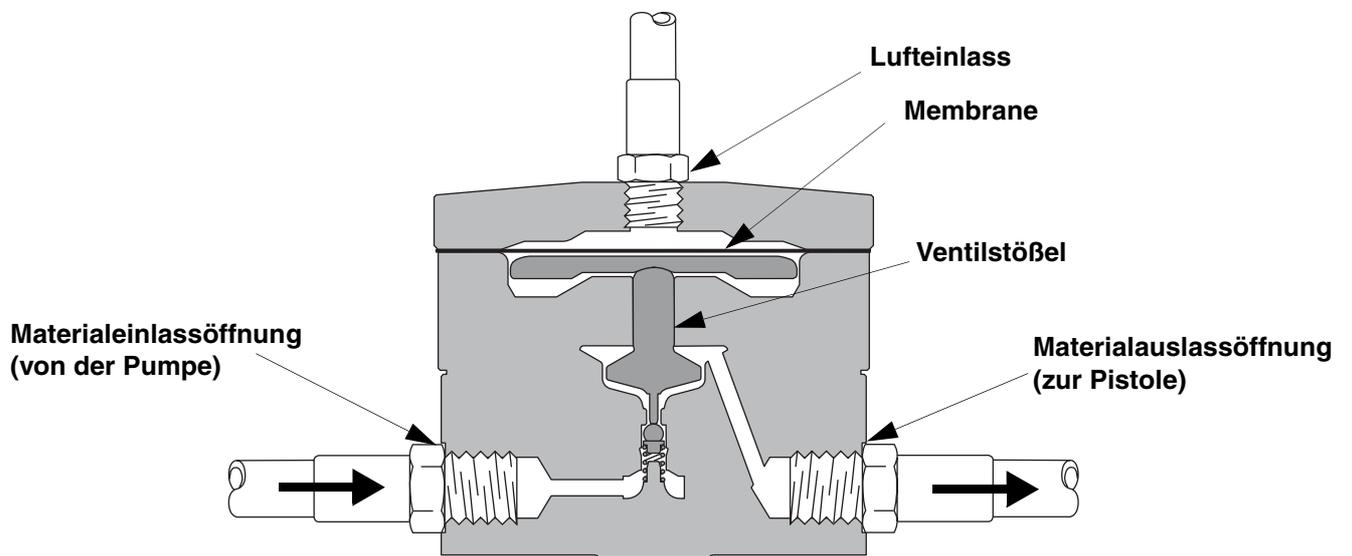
Schnittansicht eines mechanischen Gegendruckreglers
